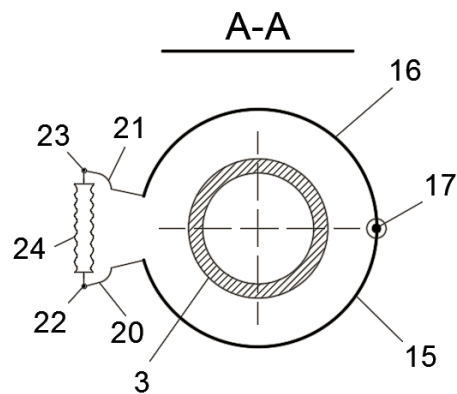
Схема подъемного участка дефлегматора: 3 – подъемный участок дефлегматора; 11 – теплоизоляционный кожух генераторного узла; 13 и 14 – шайбы крепления дополнительного кожуха; 15 и 16 – створки дополнительного кожуха; 17 – ось крепления дополнительного кожуха; 18 – паз для оси; 19 – отверстие для оси; 20 и 21 – полуовальные пластины; 22 и 23 – оси крепления; 24 – сиффон
